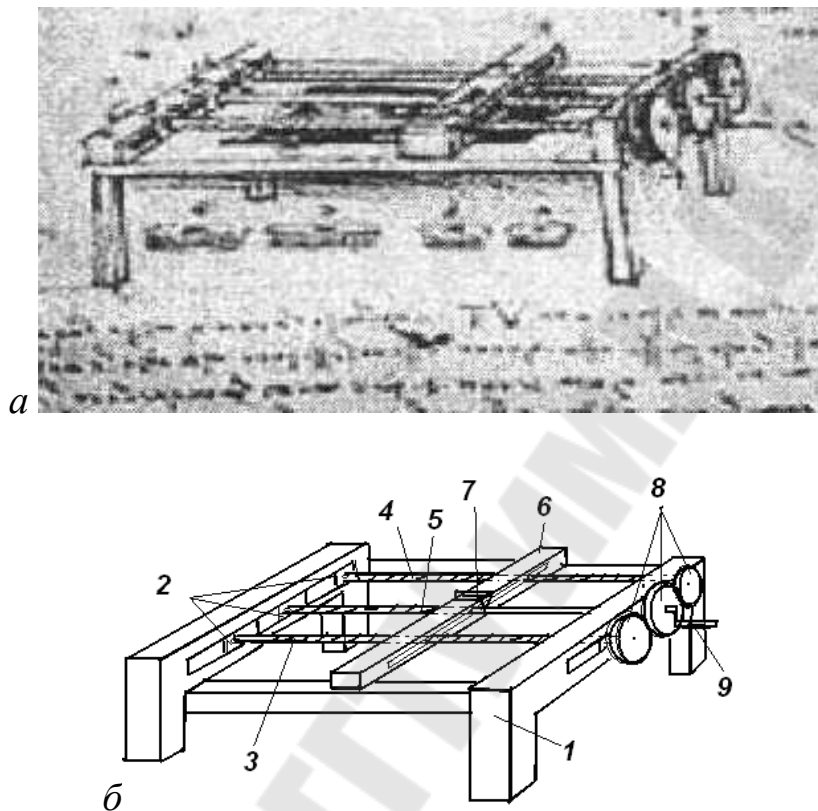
Рисунок Леонардо да Винчи токарно-винторезного станка(а) и его схема (б) : 1 – станина, 2 – блоки подшипников, 3, 4 – винты, 5 – заготовка, 6 – брусок со встроенными гайками, 7 – резец, 8 – сменные зубчатые колеса, 9 – рукоятка.
